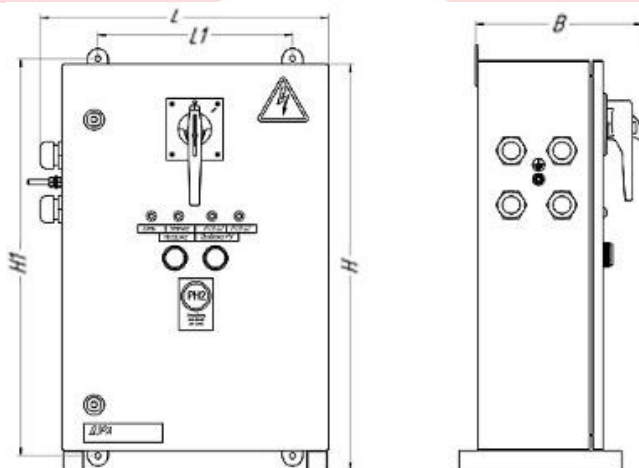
Общий вид, габаритные и установочные размеры АОРН-3Д (4Д)
